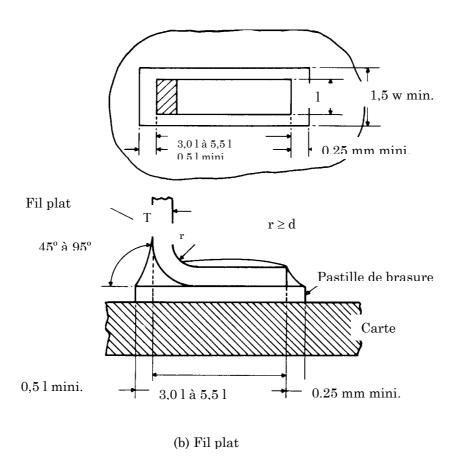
Dimensions théoriques des terminaisons à recouvrement à surface unique
